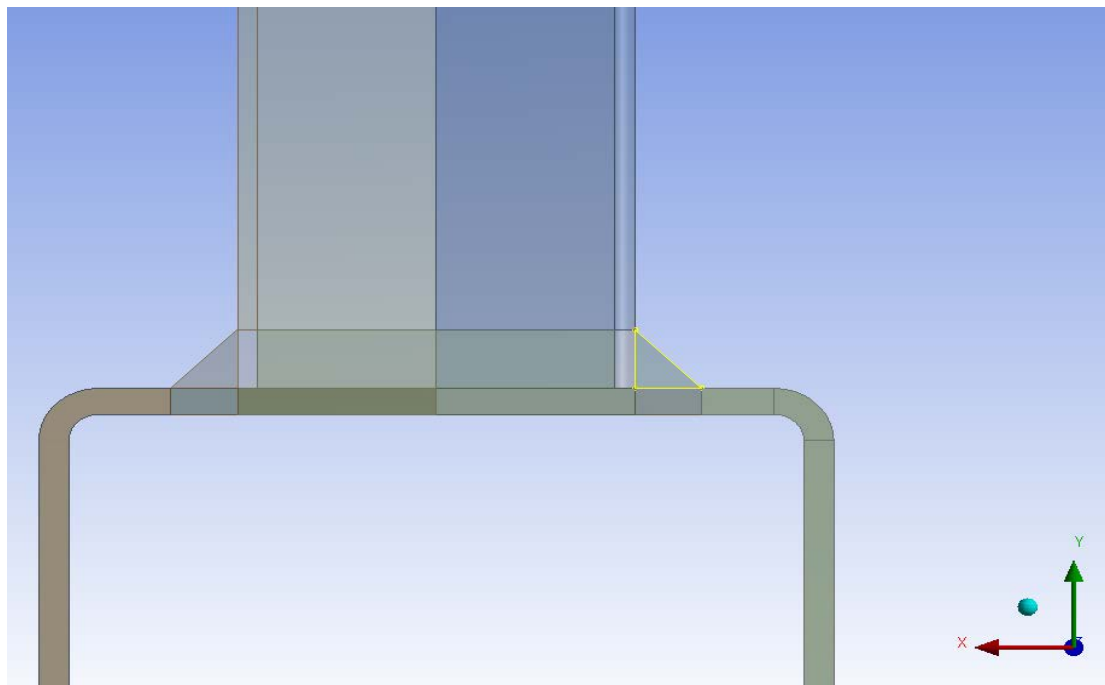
Modelo 2. *Sketch* de la soldadura
